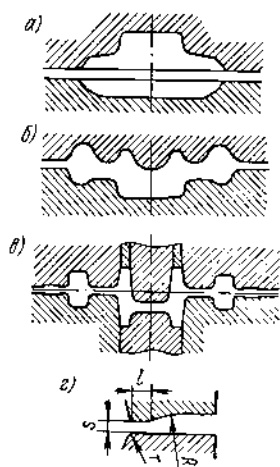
Формы последовательных ручьев штампа для поковки шестерни: а — подготовительный ручей; б — черновой ручей; в — чистовой ручей; г — форма наиболее распространенной канавки для облой
